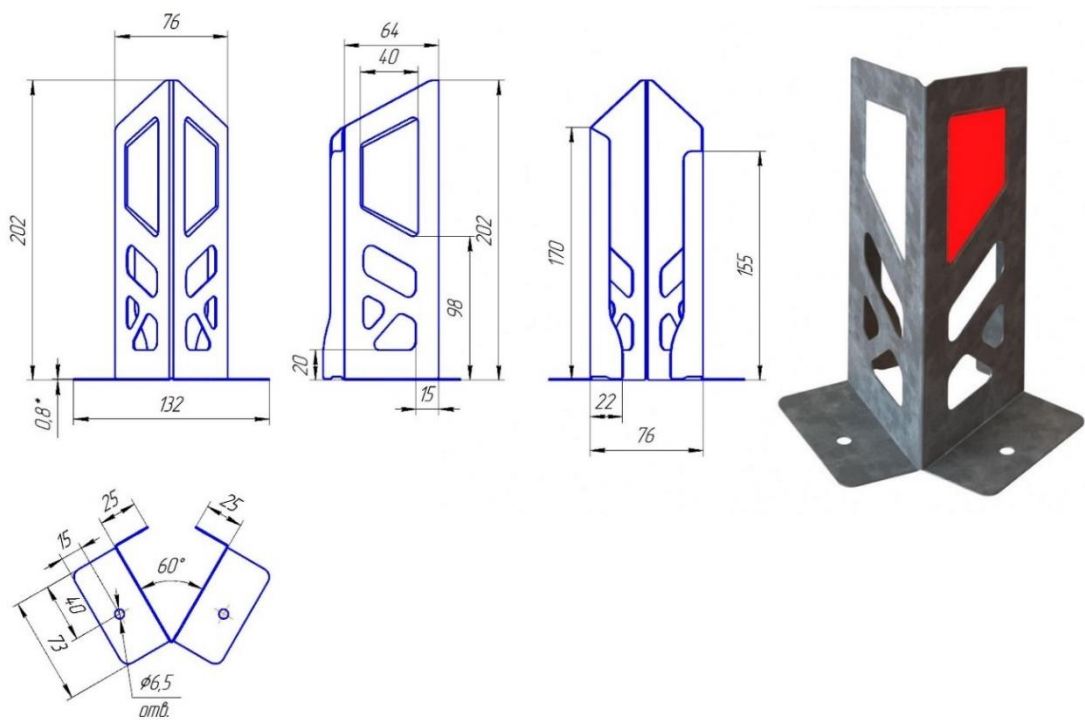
Конструкция и размеры световозвращателя КД5БП-БК2
